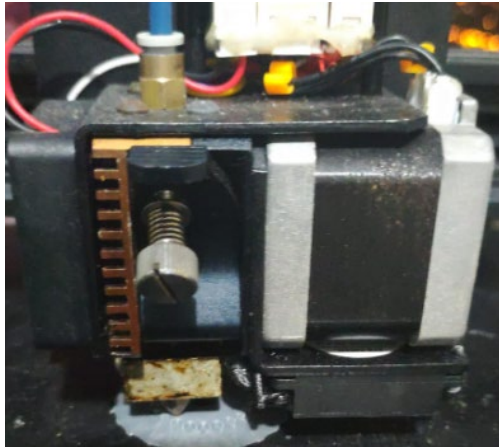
Impresión 3D conjunto de piezas en PLA
